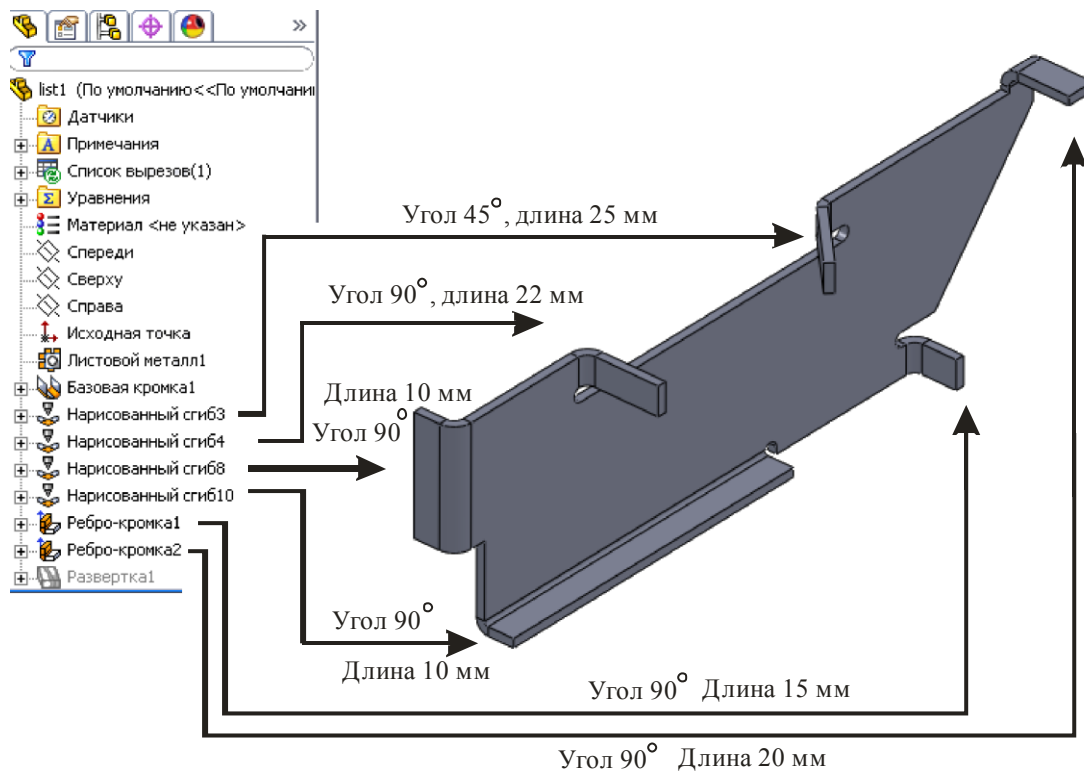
Результат построения ребер-кромки и нарисованных эскизов для заготовки задней стенки
